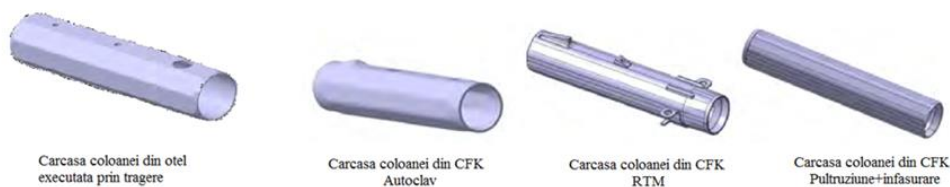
Desen CAD- carcasa coloanei de direcție în funcție de procesul de fabricație [32]
